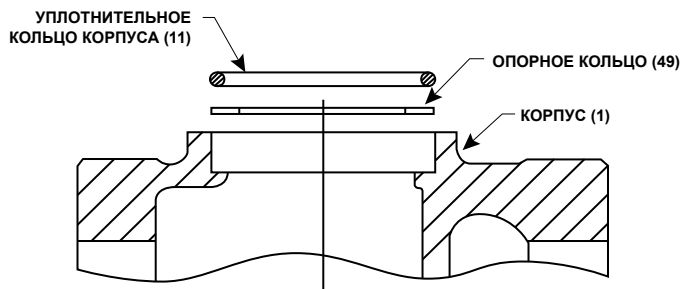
Подetailный вид корпуса с показанным размещением уплотнительного кольца корпуса и опорного кольца
